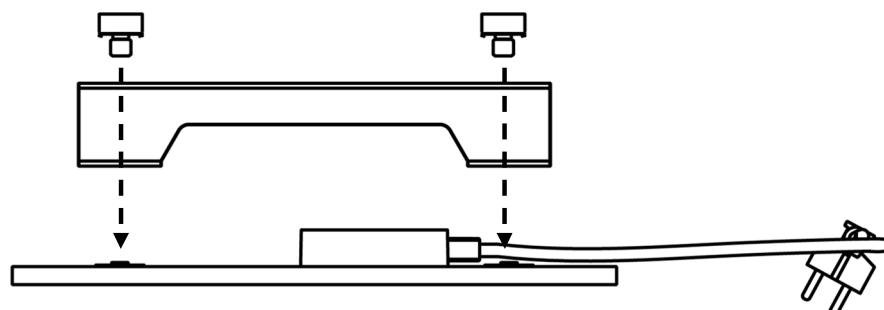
Befestigung der Halterungen (AGH0011S, AGH0012S)
